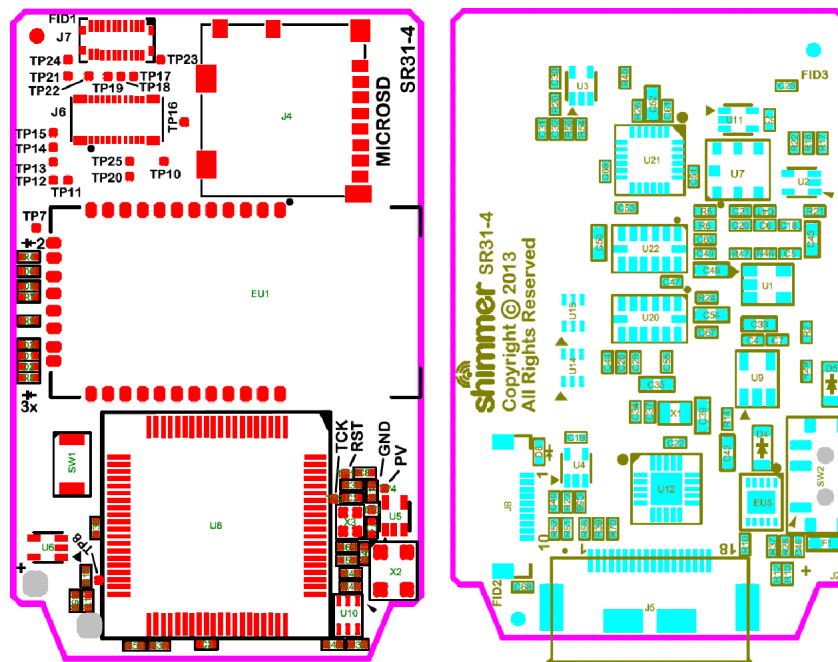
Shimmer3 mainboard layout (a sinistra vista dall'alto, a destra dal basso)
